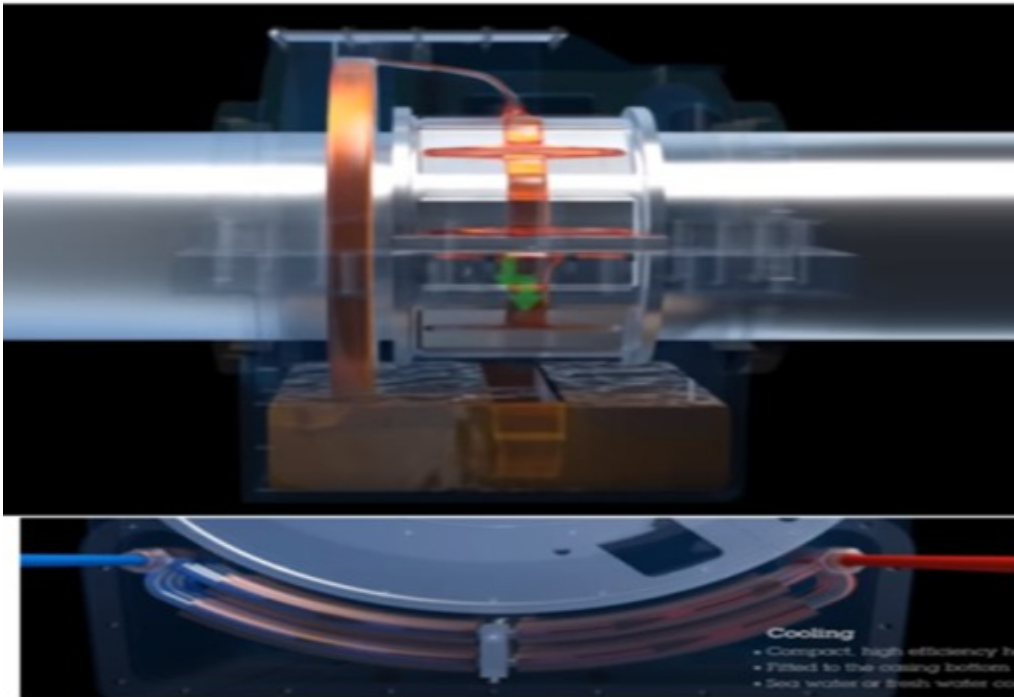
Διάταξη κυκλοφορίας ελαίου [*Michell Bearings hydrodynamic propeller shaft bearing and thrust block - YouTube*]
